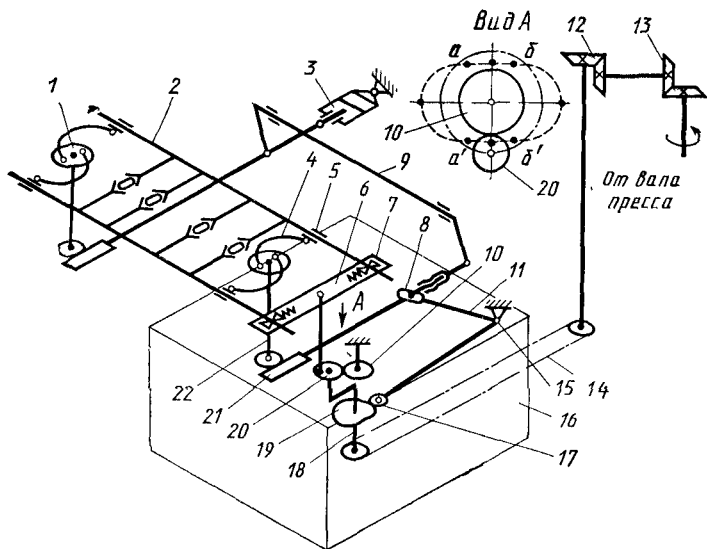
Двухкоординатное грейферное передающее устройство с приводом от вала прессы
